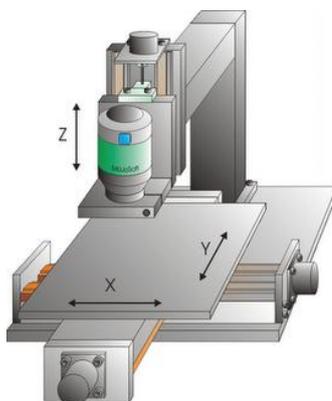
Станок ЧПУ с движущейся по оси Z фрезерной частью
